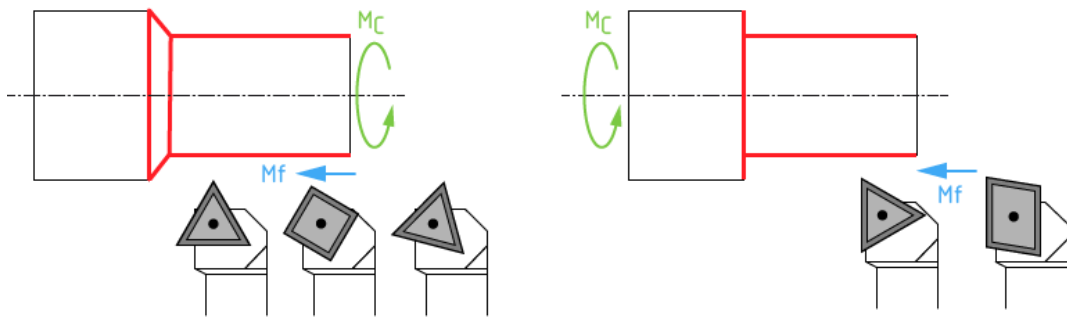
Opération de Chariotage et des outils de coupe [1].
